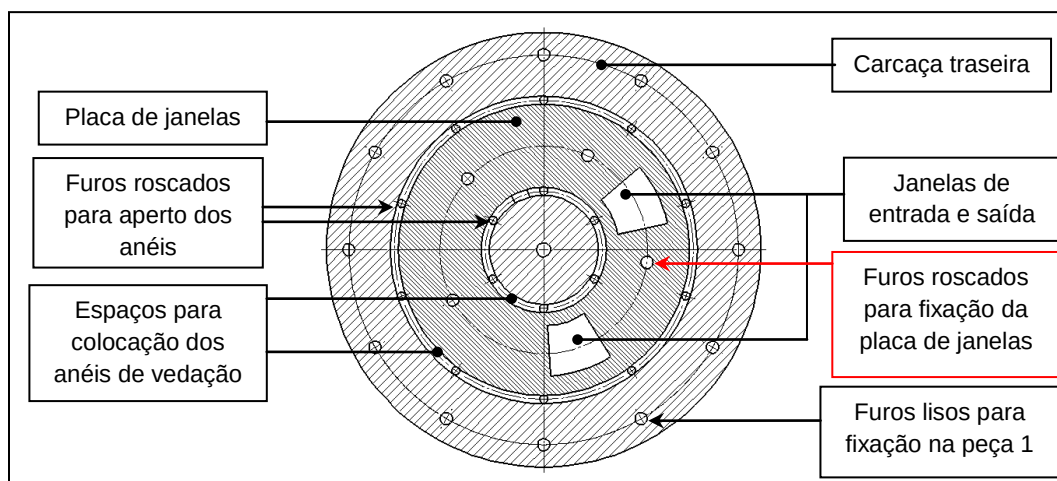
Vista de montagem em corte da carcaça traseira e da placa de janelas.
